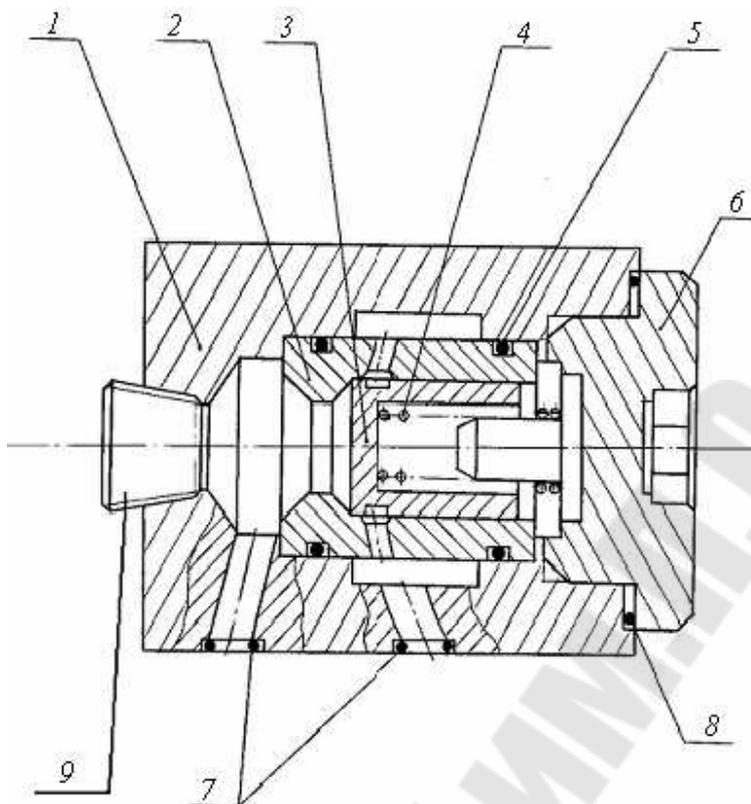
Блок присоединительный клапана обратного типа БПВ-6КО
